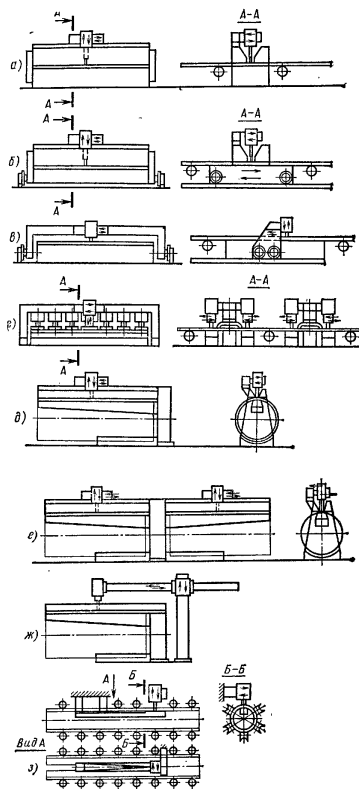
Типовые схемы компоновок установок и станков для электродуговой сварки прямых стыковых швов с прижимом свариваемых кромок
